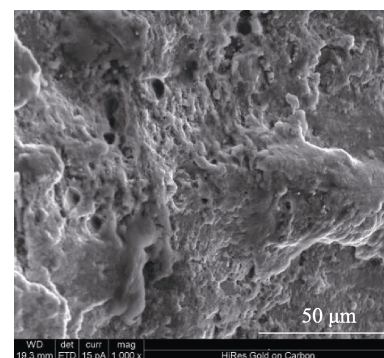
预腐蚀后的断口快速断裂区形貌
